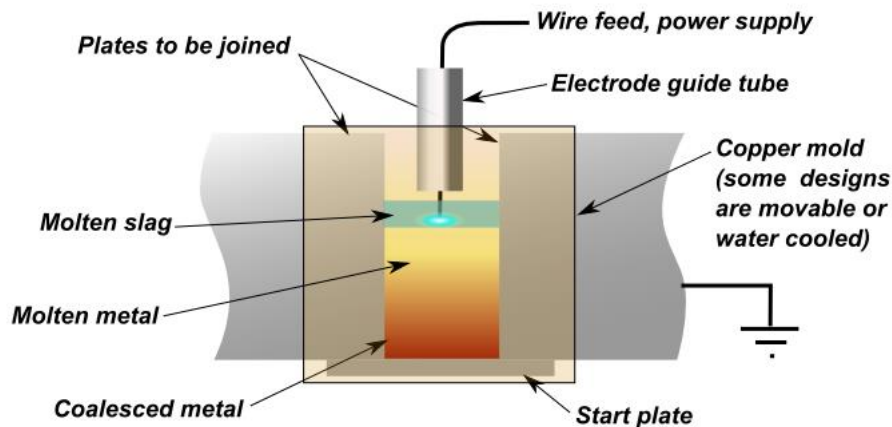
Soldadura por Electroescoria (ESW). (23)
